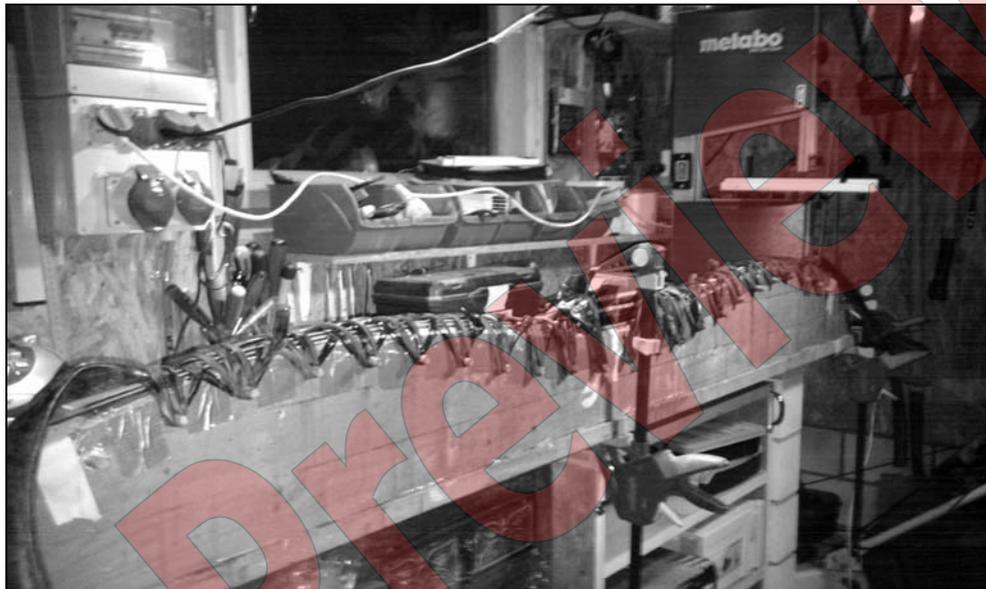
Nachdem wir das Griffstück mit einer Zwinde gesichert haben können wir nun die Wurfarme fertig laminieren. Mit den Gummibändern pressen wir die Lamine in die Form
